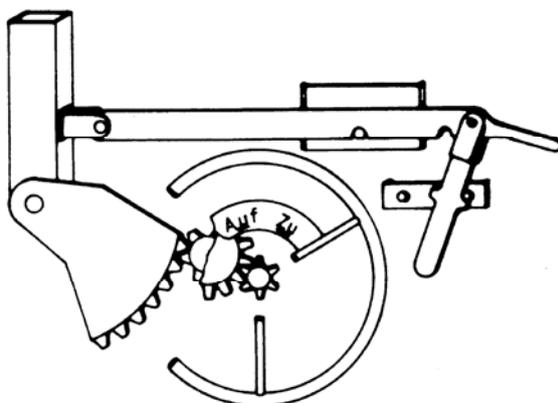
„Grundstellung“; das Schwenkdach ist verriegelt und geschlossen.
